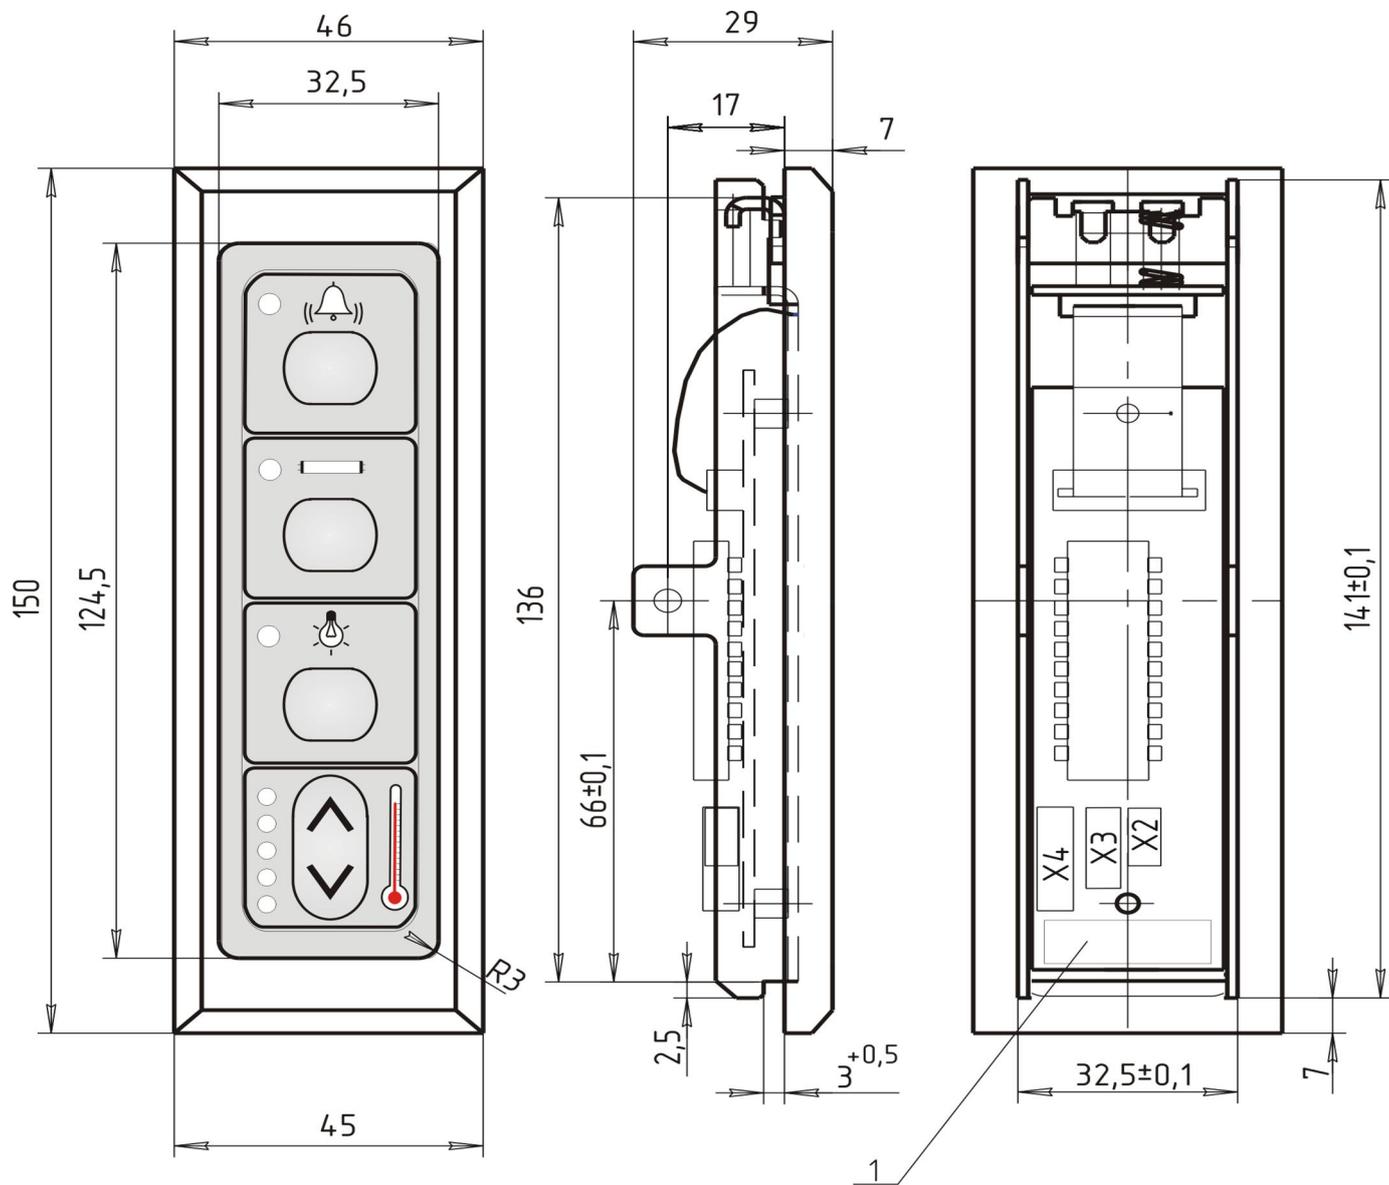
Внешний вид, габаритные и присоединительные размеры ПЭК-1.01
